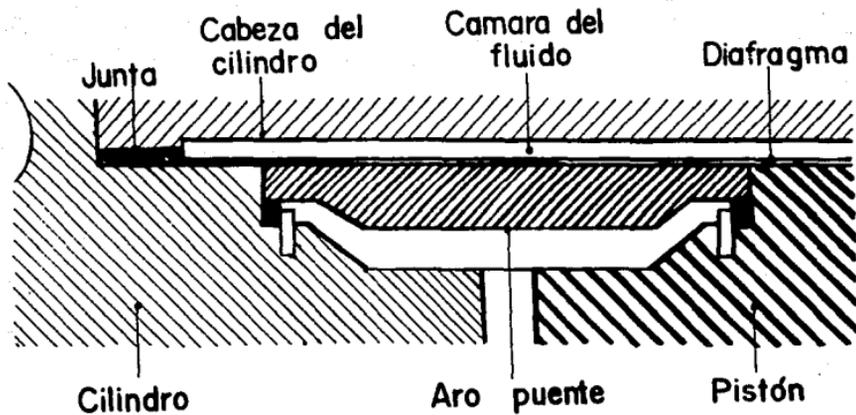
Sección que muestra al detalle el aro puente de la Cápsula
